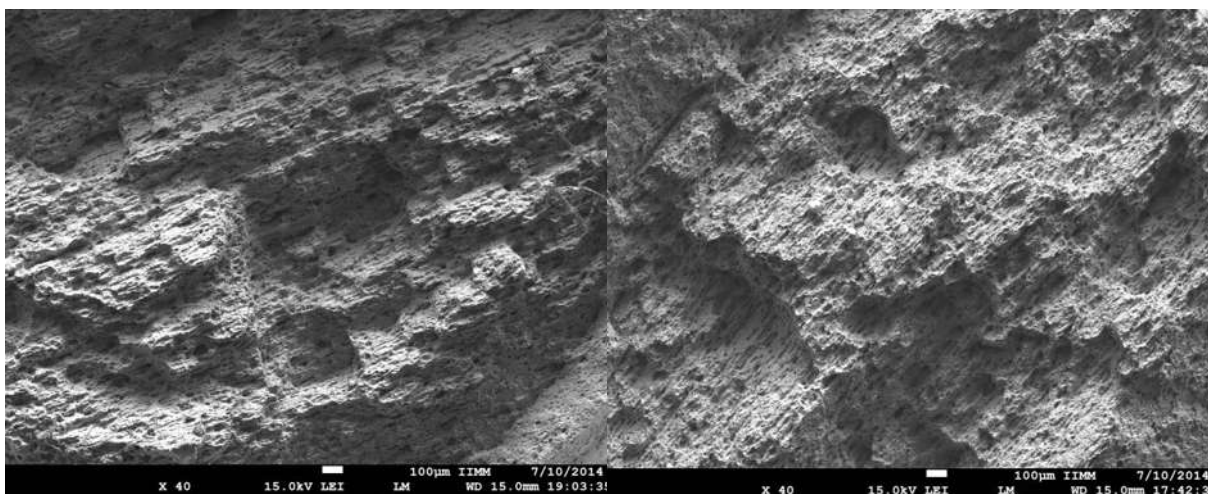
23.- Fractografía de la soldadura 5-1(uni3n simple, condici3n 1).
